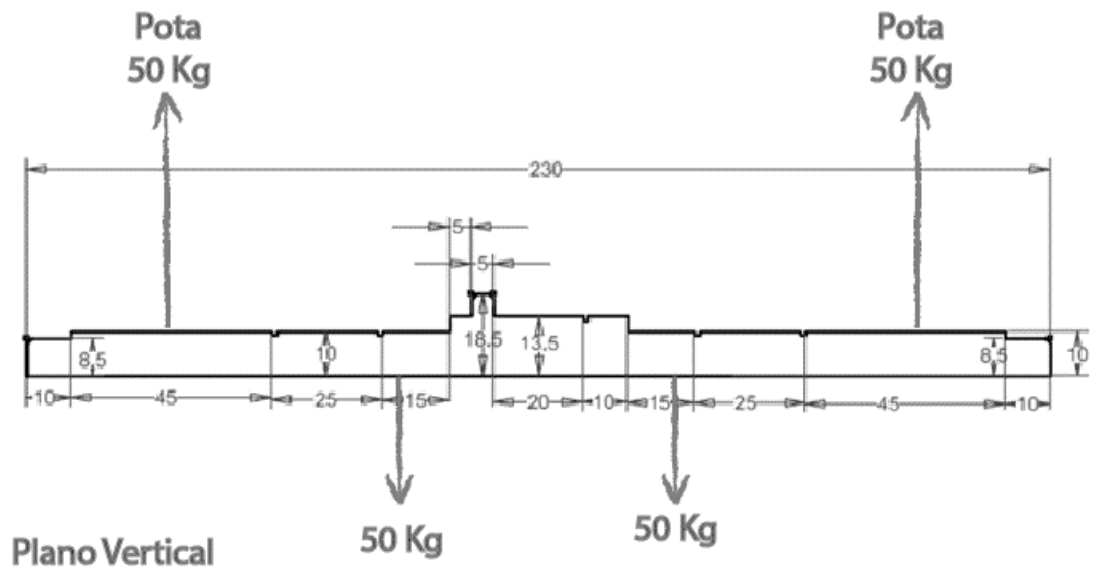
Fuerza en el eje de carrete en el plano vertical. Fuente. – Elaboración propia.
